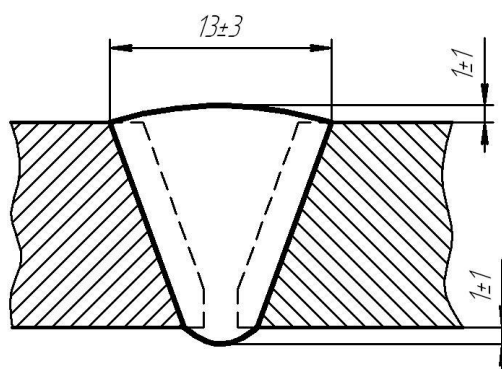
Геометрия получившегося при сварке шва
